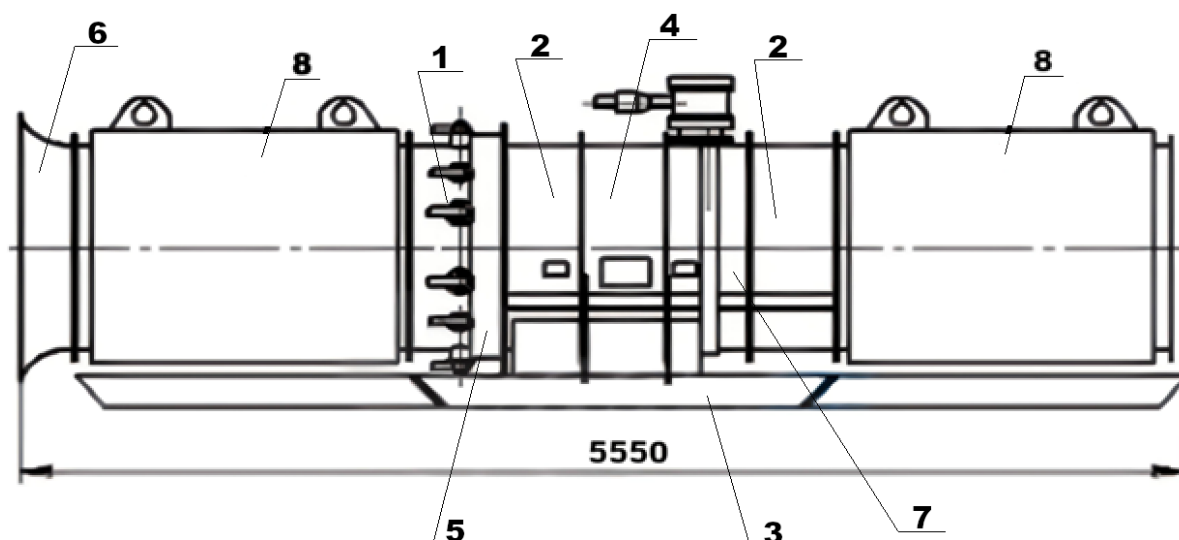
Вентилятор ВМЭ2-10А: 1 – аппарат направляющий; 2 – рабочее колесо; 3 – салазки; 4 – взрывозащищенный электродвигатель; 5 – устройство противосрывное; 6 – коллектор с коком и предохранительной решеткой; 7 – аппарат спрямляющий; 8 – глушитель шума
